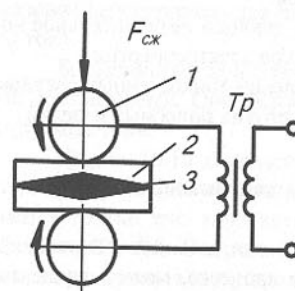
Шовная (роликовая) сварка
